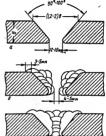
Заварка трещины на детали, подвергаемой механической обработке:
